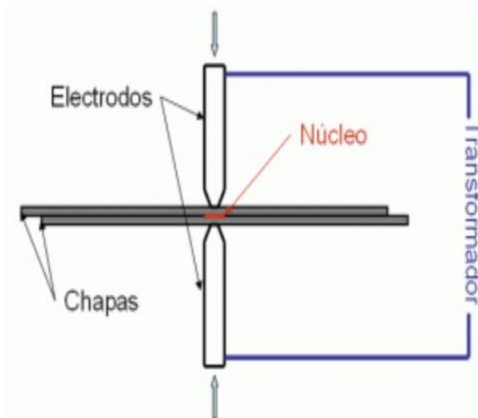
Esquema soldadura por puntos. [1]
